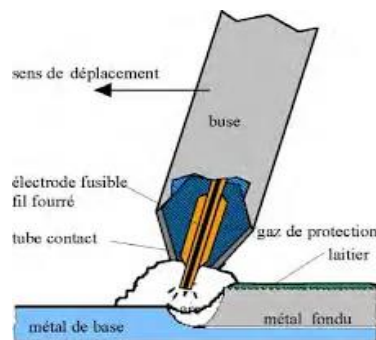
Schéma d'assemblage par soudage .
